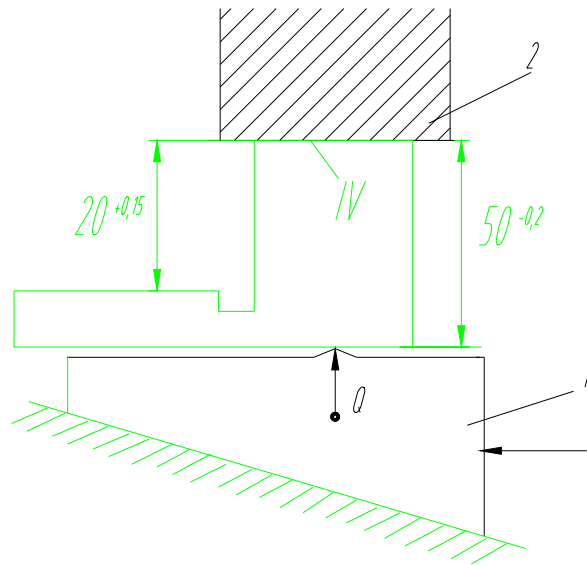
Схема усовершенствованного фрезерного приспособления:
